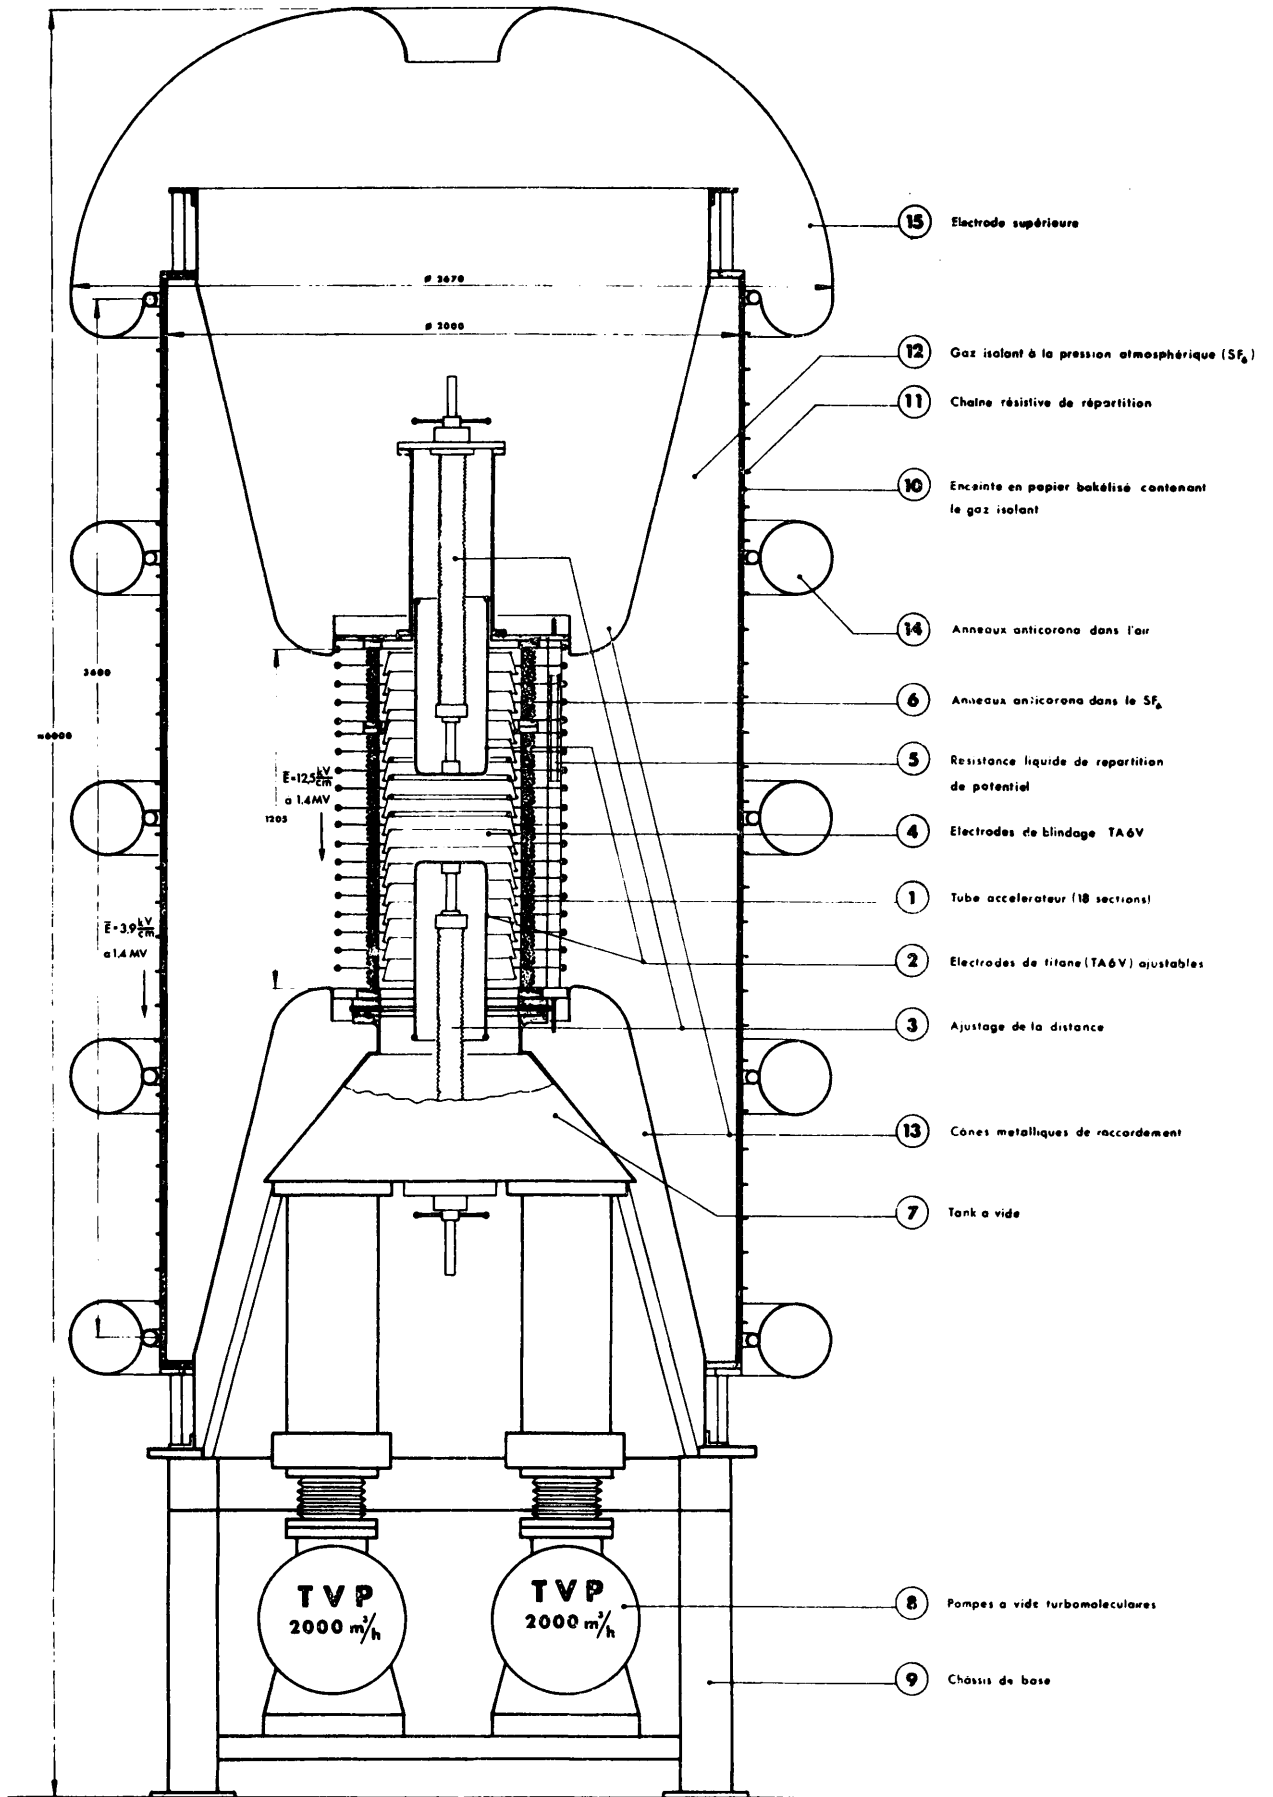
Essai Berthe - Coupe du dispositif d'essai
